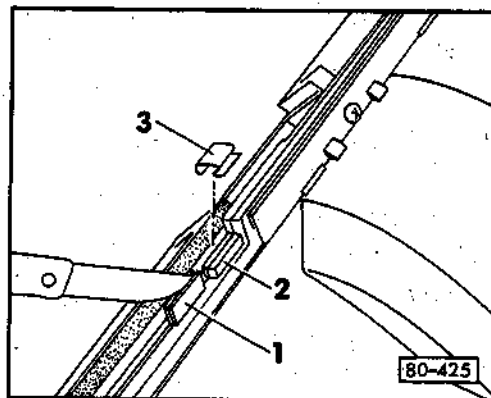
Klappenkastenoberteil und Klappenkastenunterteil zerlegen und zusammenbauen
